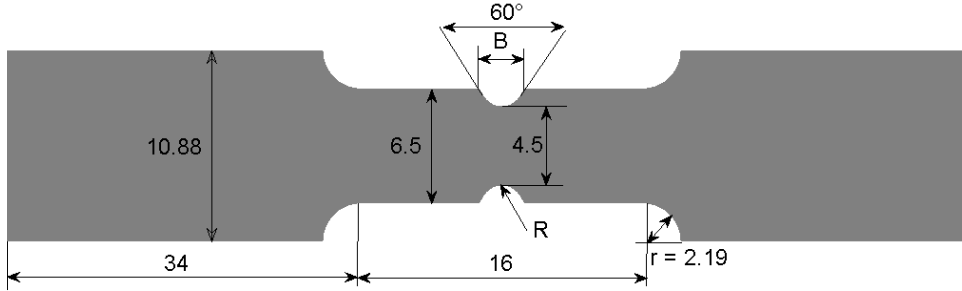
Schéma des éprouvettes plates entaillées
